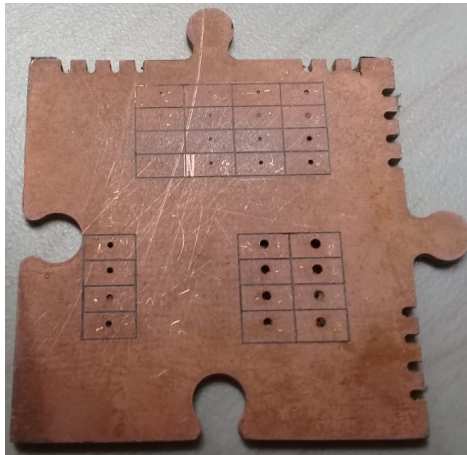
PCB prueba para metalización de vías por electrodeposición.
